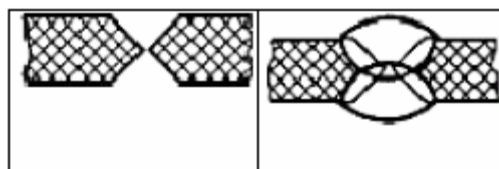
Схематичне зображення зварного з'єднання «С14»
